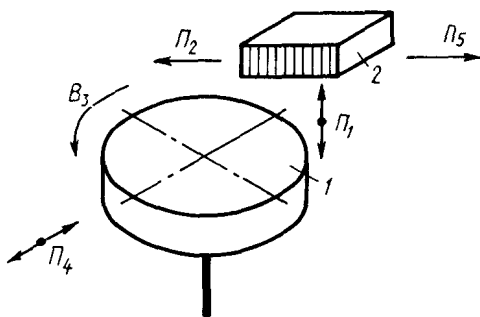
Способ обработки зубчатого колеса короткой (трехзубой) гребенкой
